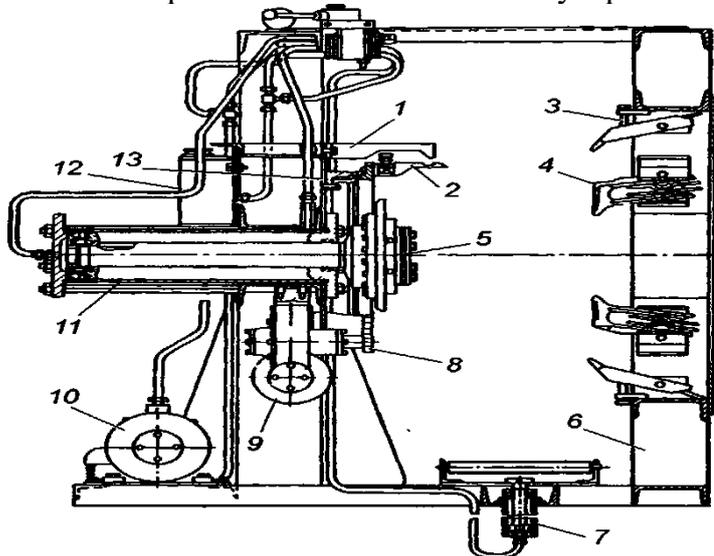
Стенд для демонтажа и монтажа шин грузовых автомобилей: 1 - упор; 2 - съемник замочного кольца; 3 - винт; 4 - лапа; 5 - пневматический патрон; 6 - рама; 7 - гидравлический подъемник; 8 - зубчатое колесо; 9 - редуктор; 10 гидравлический привод; 11 - гидравлический цилиндр; 12 бачок; 13 обечайка
